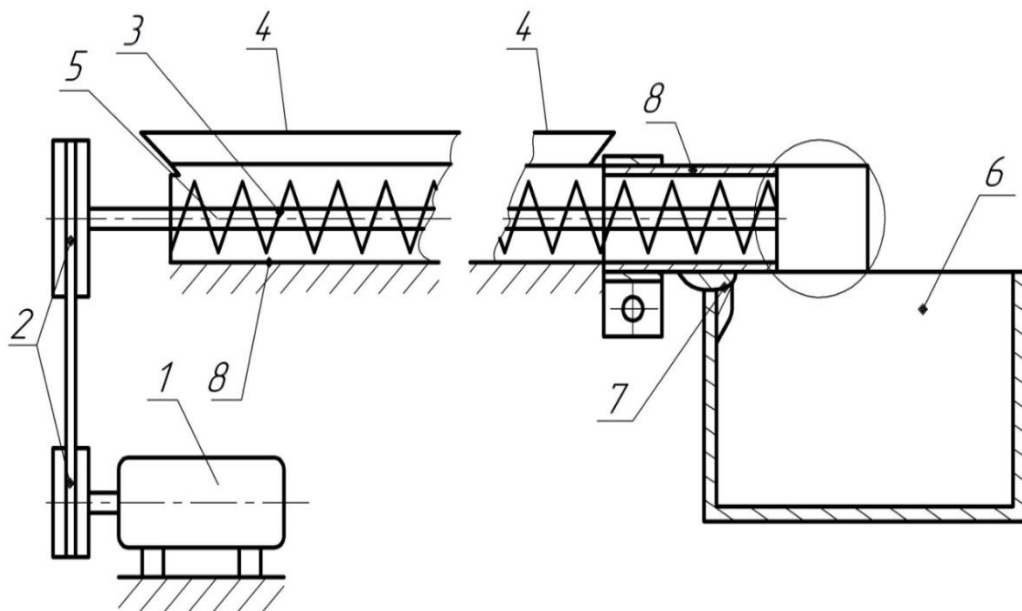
Принципова схема роботи шнекового транспортного механізму
